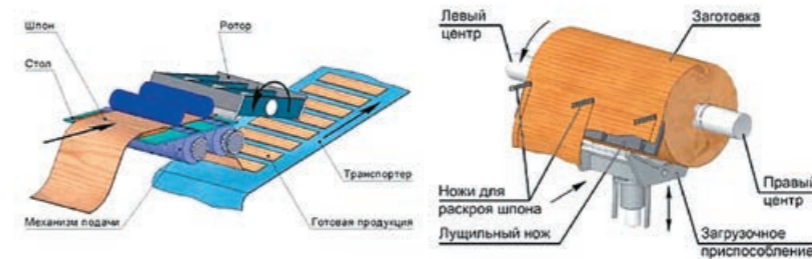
Лущильный станок и ножницы для рубки шпона на тарные дощечки (МАГР)
